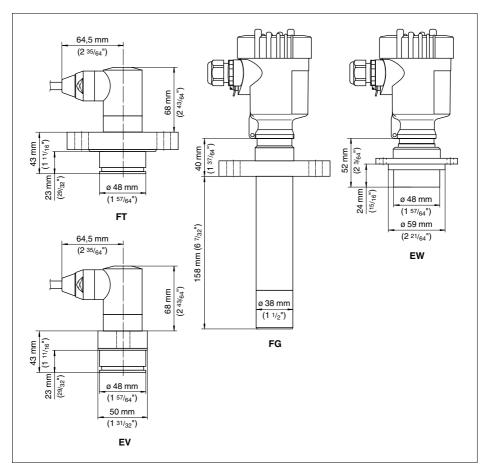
VEGABAR 64 - Tubusanschluss für die Papierindustrie: EV/FT = absolut frontbündig für Stoffauflauf (EV: Flansch 2-fach abgeflacht), FG = Tubus für Kugelhahnarmatur, EW = Flansch für Manometerauge
